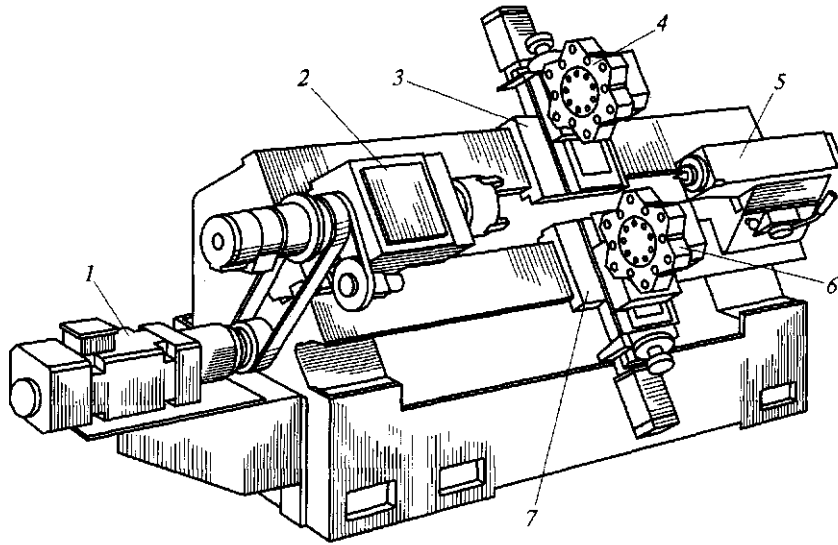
Токарно-револьверный станок с ЧПУ с наклонным расположением суппортов:
